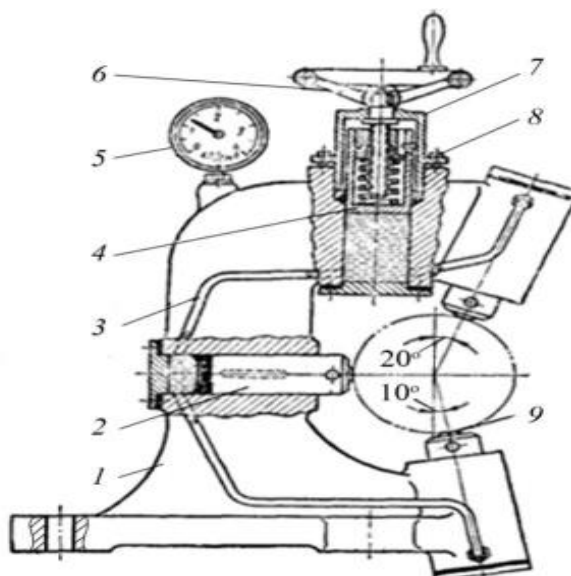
Люнет-виброгаситель: 1 – корпус; 2 – поршни; 3 – трубы; 4 – загрузочный поршень; 5 – манометр; 6 – рукоятки; 7 – крышки; 8 – болты; 9 – ролики
